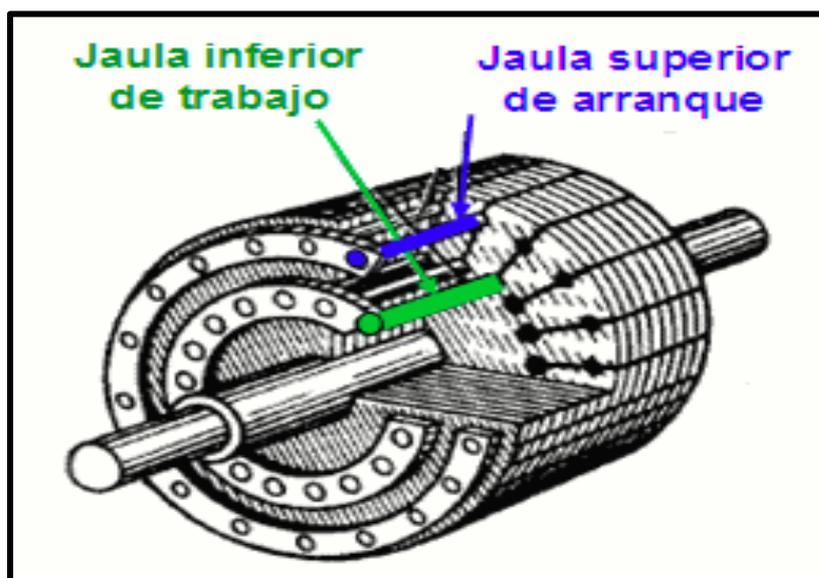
Rotor de jaula de ardilla doble. Fuente: [9]
